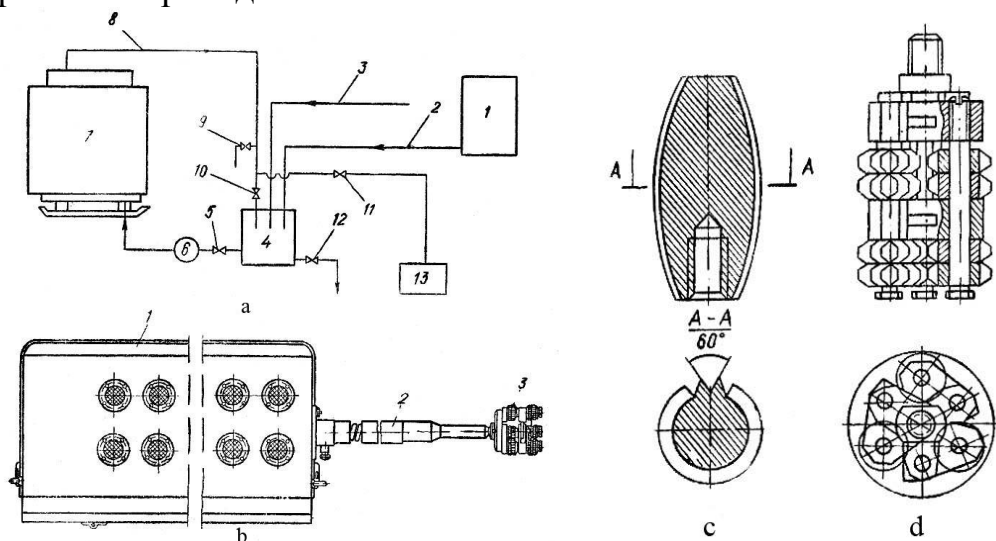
Способи очищення обладнання від накипу: а – схема хімічного очищення котлів з примусовою циркуляцією розчину: 1 – бак з кислотою; 2 – кислотна трубка; 3 – водяна труба; 4 – промивний бак; 5, 10, 11 – крани; 6 – насос; 7 – котел; 8 – зворотний трубопровід; 9 – кран відби-рання проб; 12 – спусковий кран; 13 – дренажна бак; б – пристрій для очищення котлів і пароутворювачів від накипу механічним способом: 1 – силова частина пристрою (електродвигун із з'єднувальною муфтою); 2 – гнучкий вал; 3 – змінна головка; с, d – еліпсоїдна і розкидна головки для механічного очищення кип'ятильних труб котлів від накипу
